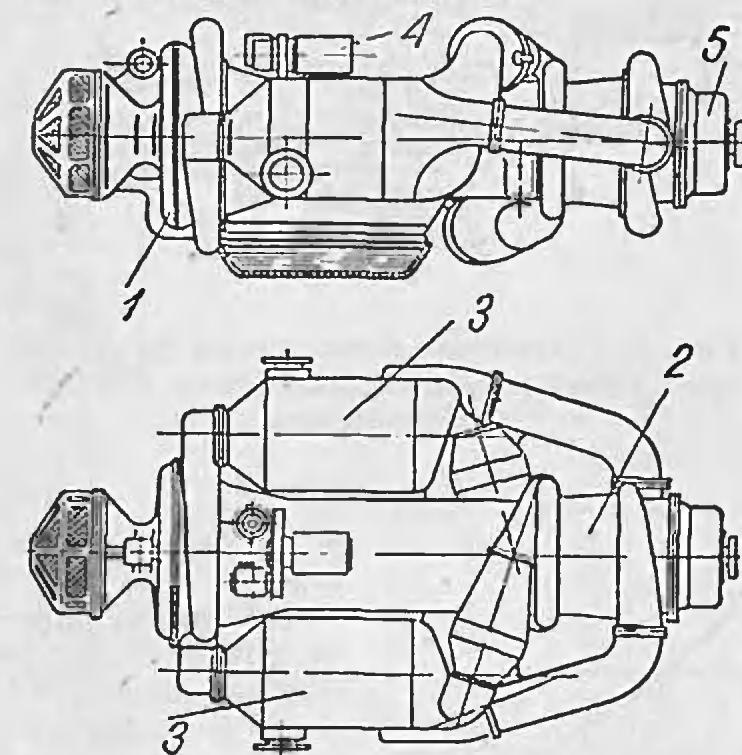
Испанский газотурбинный двигатель, предназначенный для автобуса:
